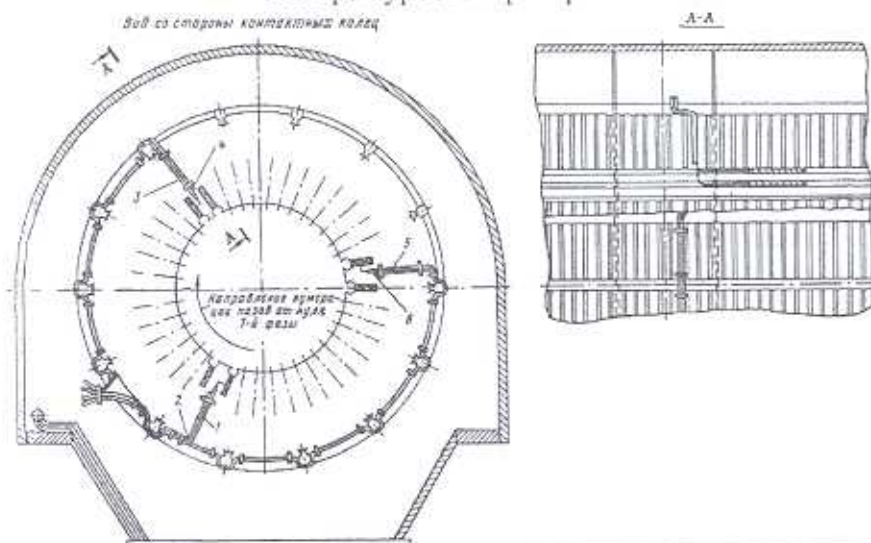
Газоплотный вывод проводников термопреобразователей сопротивления из корпуса статора:
